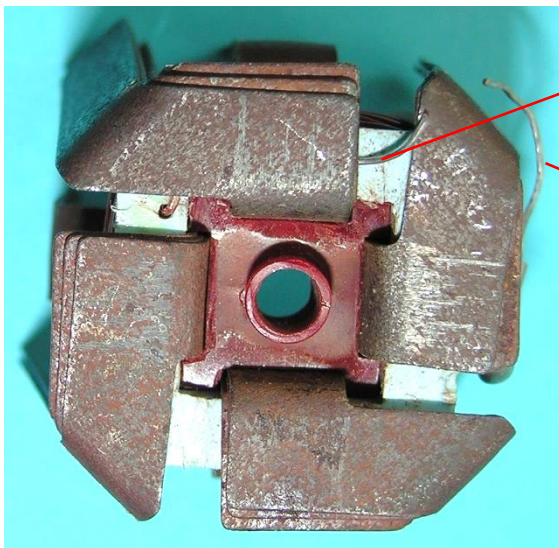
Ansichten des Formstücks zur Fixierung der Polpaare
